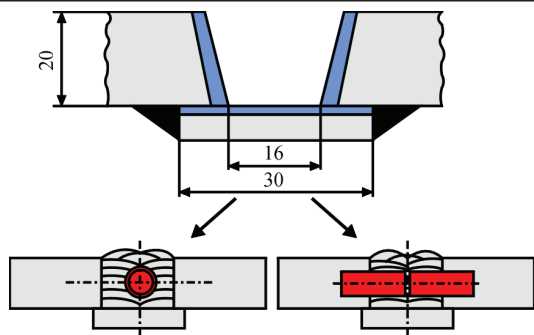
Подготовка кромок и эскизы вырезки из наплавленного металла
